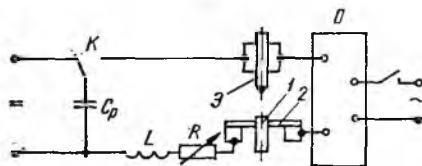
Принципиальная схема способа дуговой конденсаторной сварки плавлением неподвижным неплавящимся электродом.
